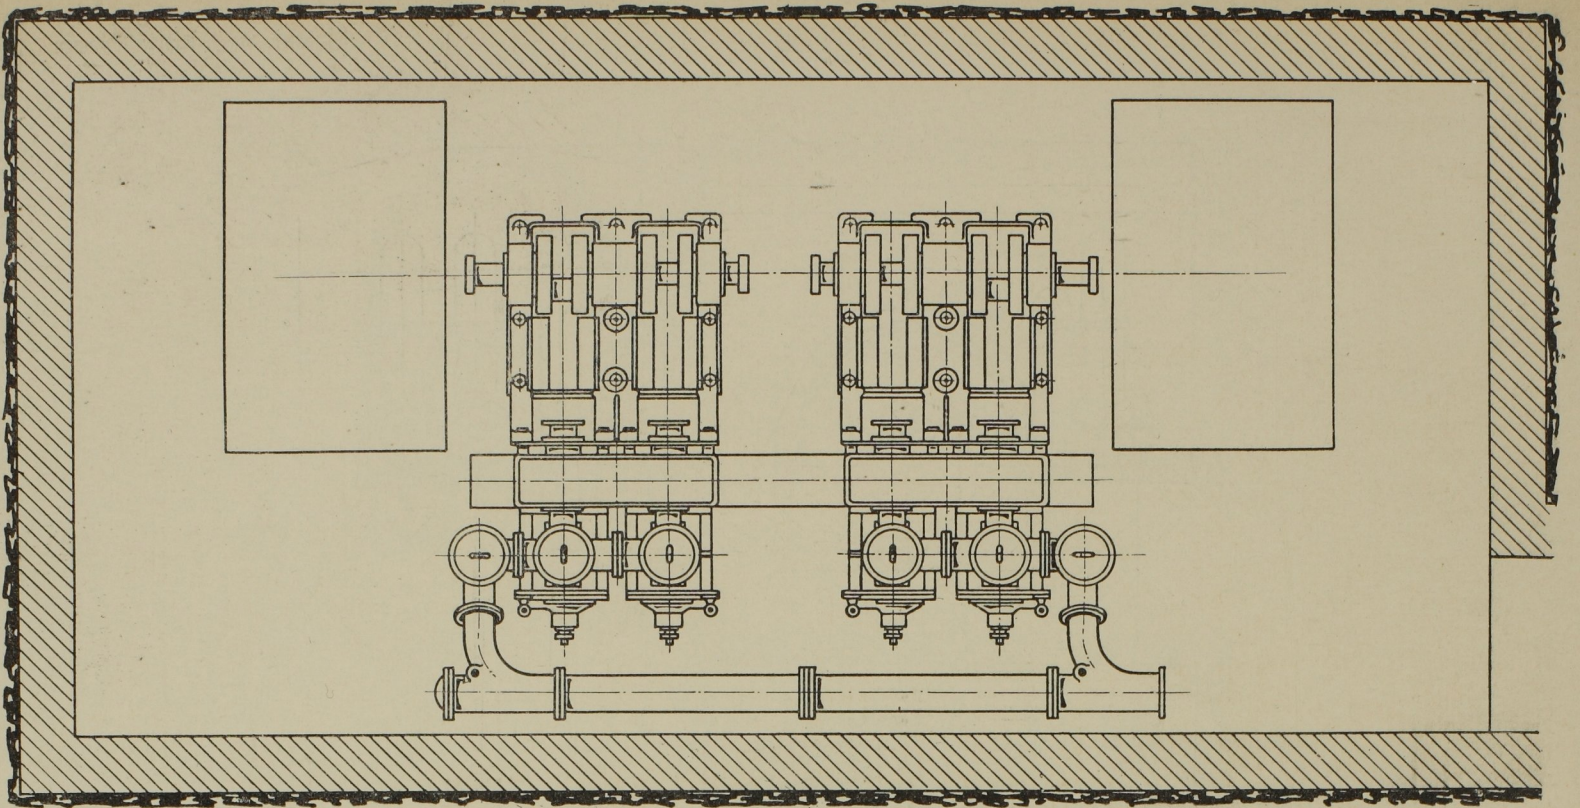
Grundriss der beiden Wasserhaltungsmaschinen. Masst. 1:80.
